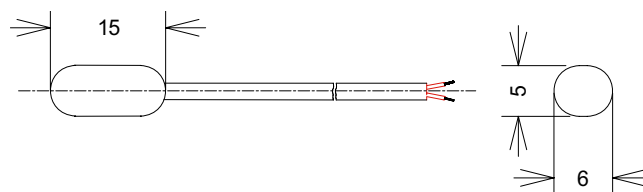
Abmessungen Anlegefühler NTC-10 im Kunststoffgehäuse
